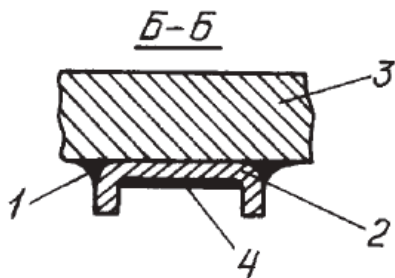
З'єднання швелерного наконечника з алюмінієвим корпусом: 1 - компаунд ЕЗК-6; 2 – швелерний наконечник; 3 – корпус; 4 – плакувальний шар міді
